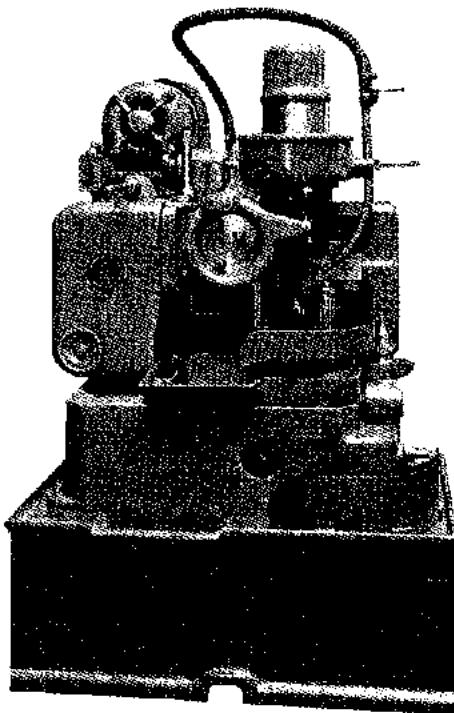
Mortajadora para engranajes (Fellows Gear Shaper Co.)
